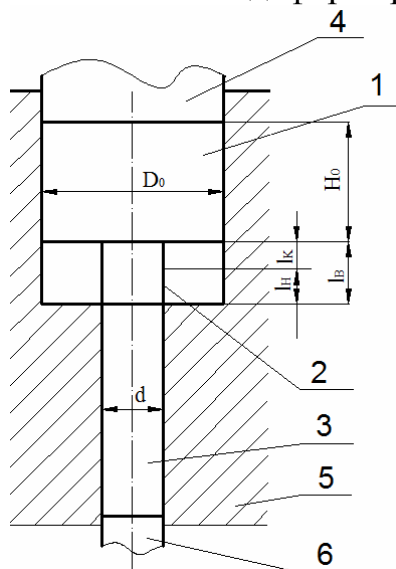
Исходное положение штампа и заготовок перед сборкой: 1 – головная заготовка; 2 – внедряемый участок (l_b) стержневой заготовки; 3 – стержневая заготовка; 4 – пуансон; 5 – матрица; 6 – выталкиватель
